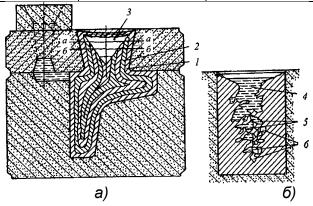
Схема образования усадочной раковины (а) и усадочной пористости (б): 1 –корка твердого металла; 2 – новый твердый слой; 3 – усадочная раковина, 4 –жидкая фаза, 5 – ячейки; 6 – небольшие усадочные раковины
